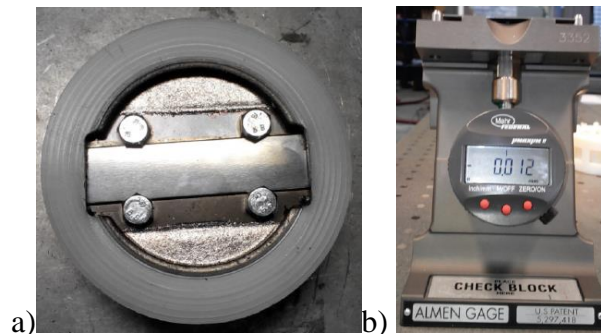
a) Porte échantillon pour plaque Almen ; b) comparateur standard pour la mesure de la flèche des plaques Almen ;
